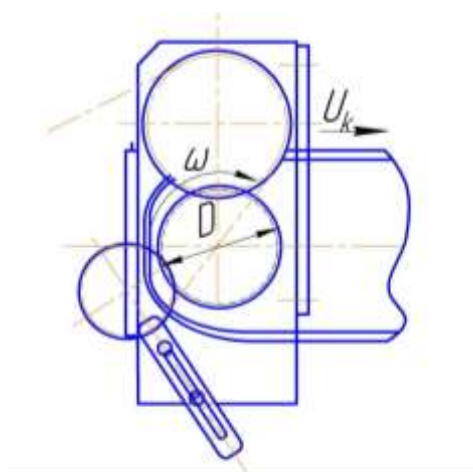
Розрахункова схема привода стрічкового транспортера
